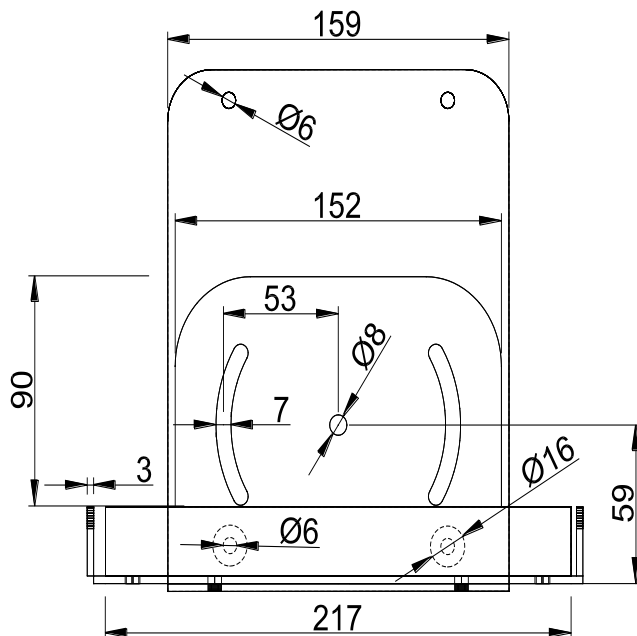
Kit de Montagem AP/Relay – Vista Frontal
